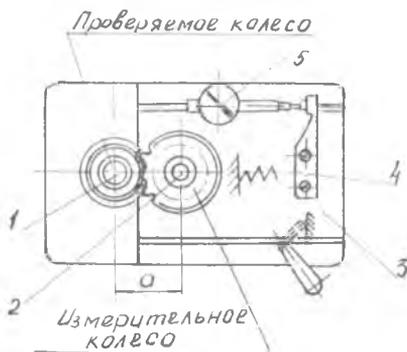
Схема приспособления для комплексной проверки цилиндрических колес
